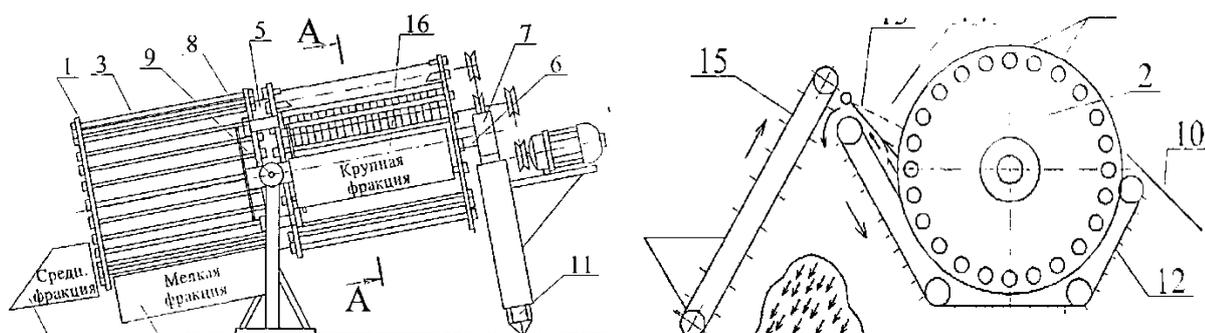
Устройство для очистки и сортировки корнеклубнеплодов:
